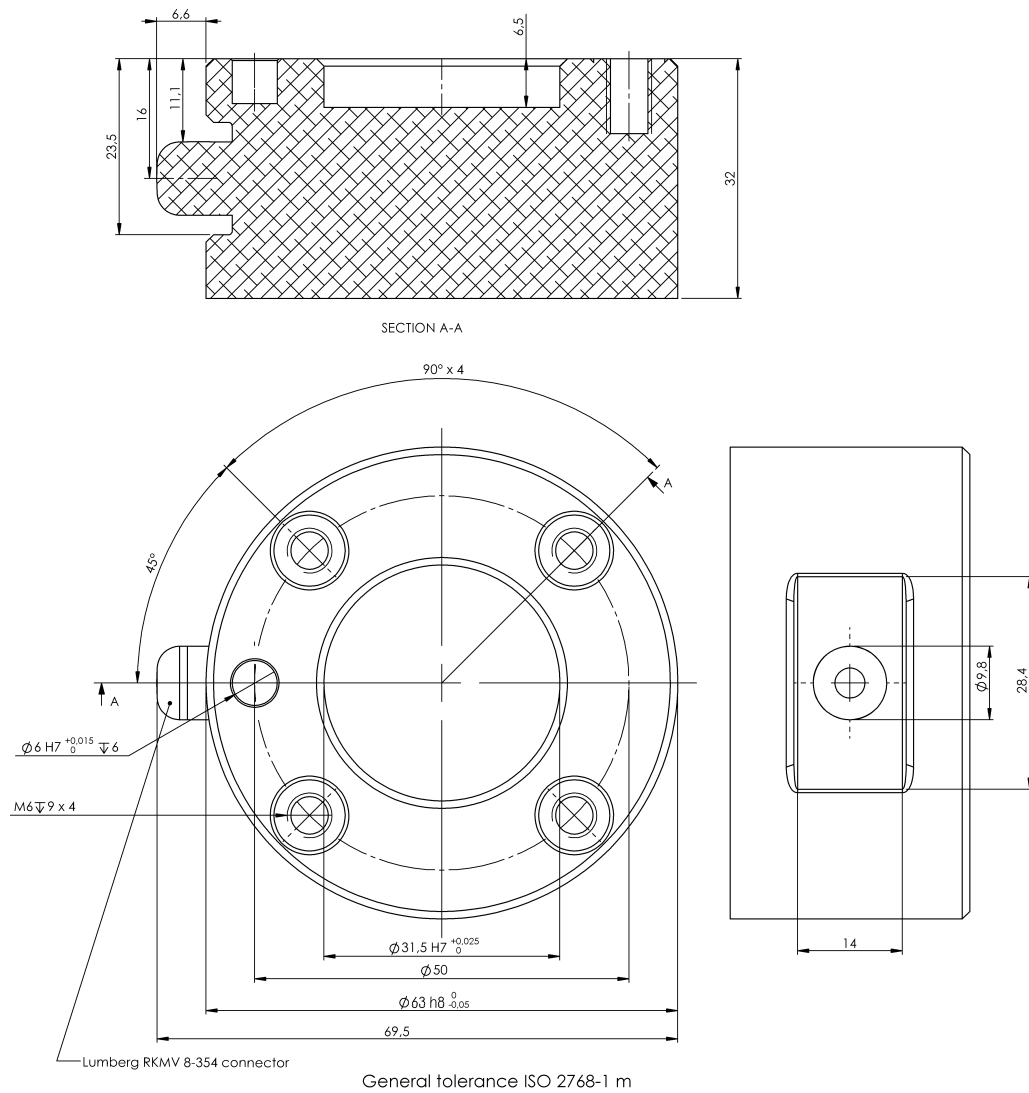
Der Werkzeugflansch, ISO 9409-1-50-4-M6. Hier wird das Werkzeug an die Spitze des Roboters montiert. Alle Maßangaben sind in mm.
